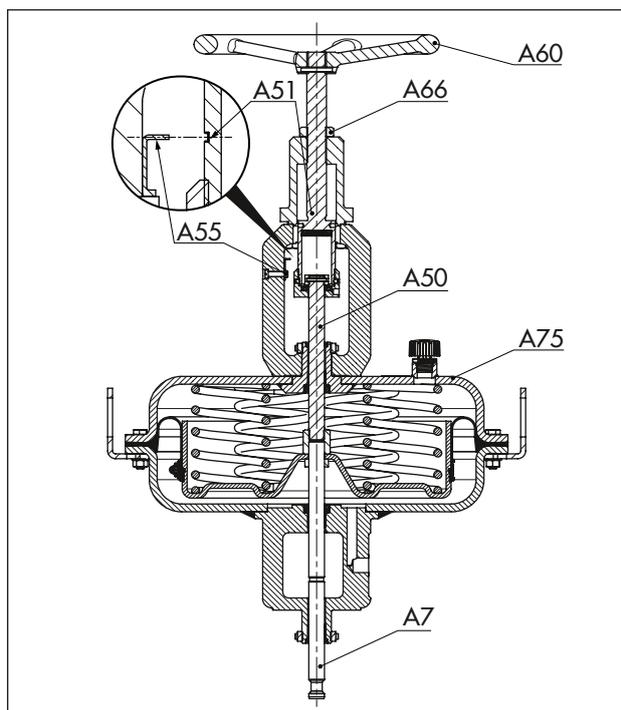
Пневматический привод Тип 3277 с ручным дублёром
